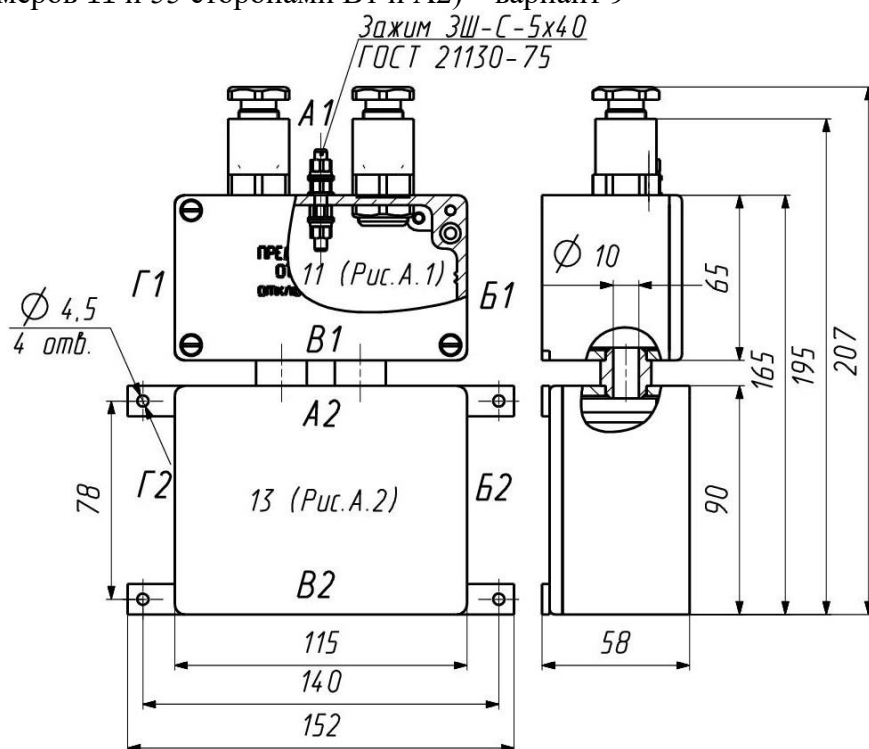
Блок корпусов и коробка клеммная ЕхБКР- А11В1/А13А2 (скрепление корпусов типоразмеров 11 и 13 сторонами В1 и А2) – вариант 10
